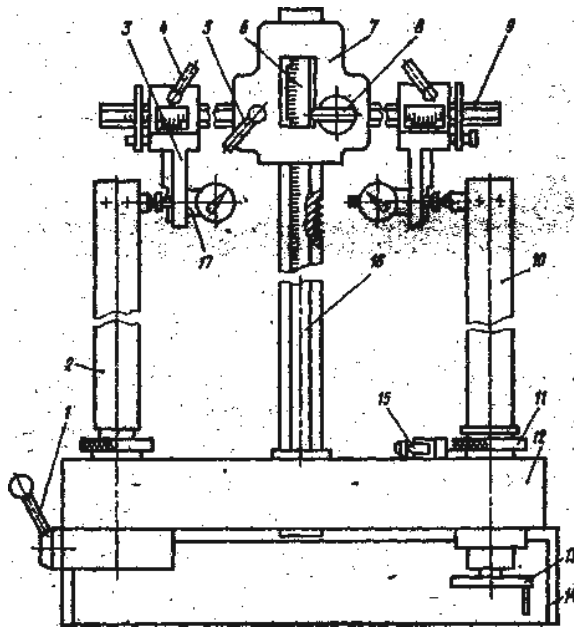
Устройство для размерной настройки инструмента мод. 8580-400
